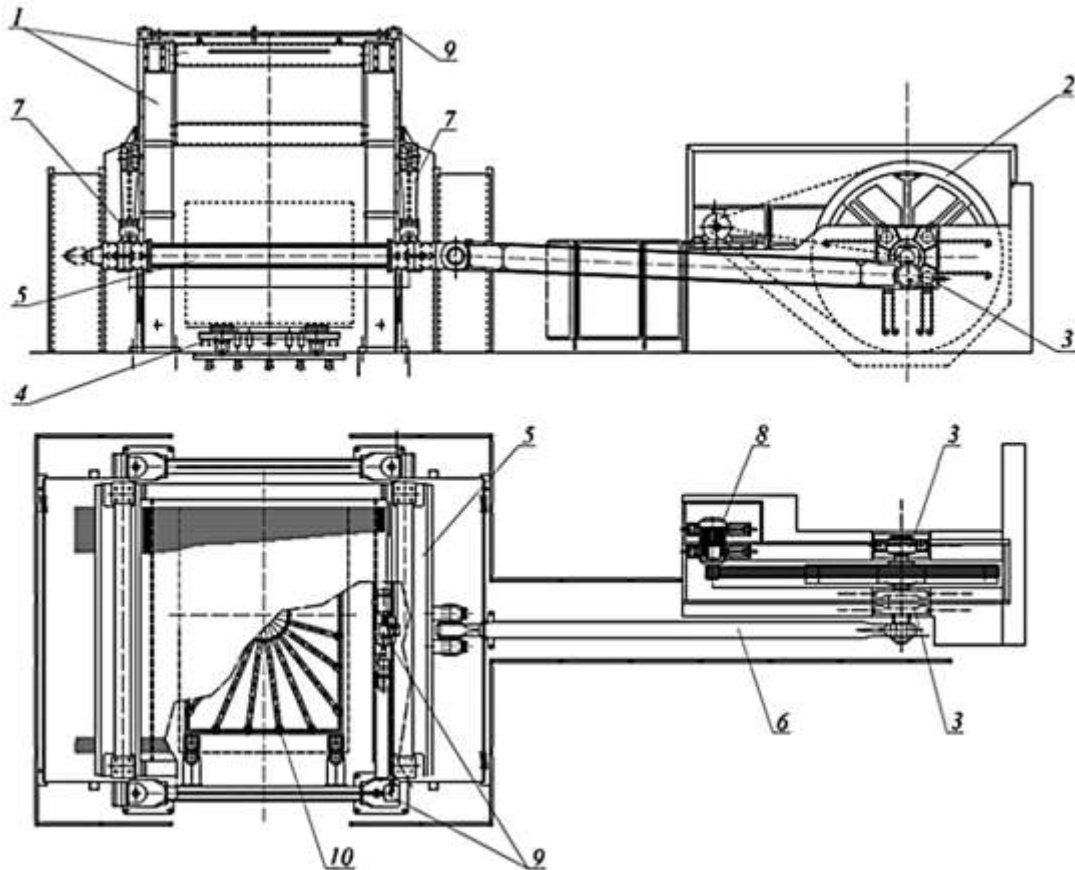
Загальний вигляд штрипсового верстату MASTERBRETON [9].
